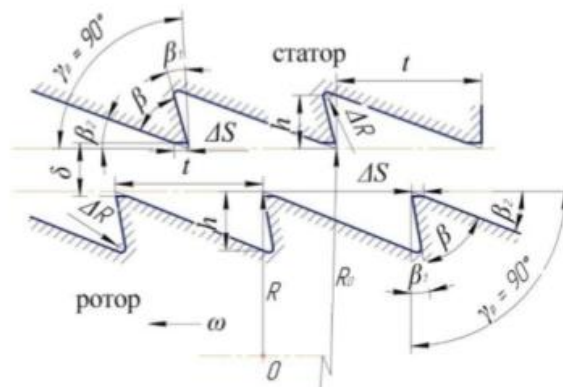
Схема зрізу зернівки робочими органами
